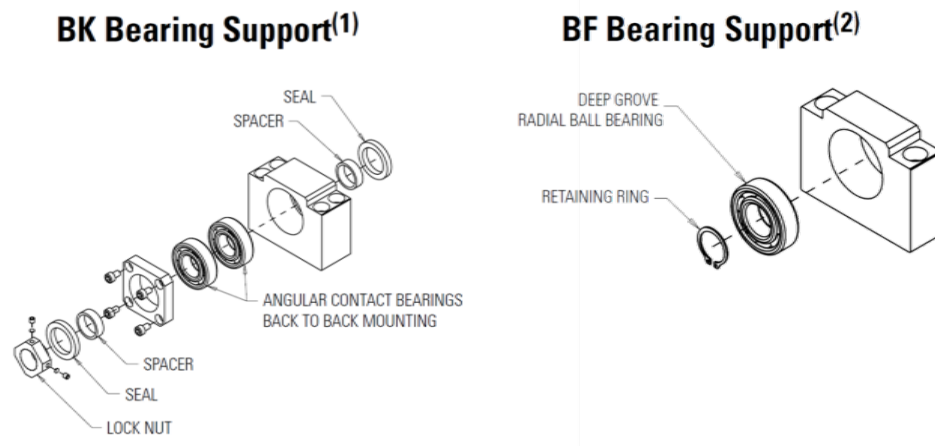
Vista explodida dos suportes BK e BF (HIWIN, 2017)
